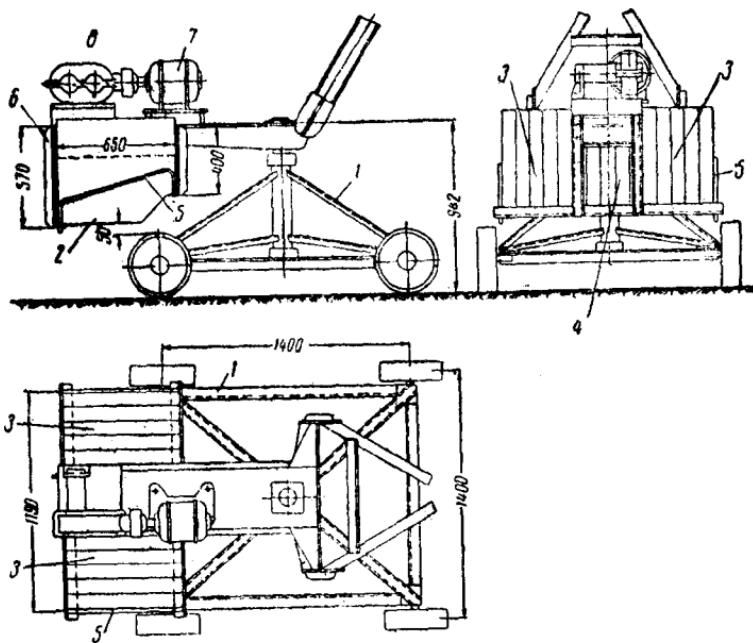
配置有钢筋混凝土块平衡锤的“先鋒牌”起重机行动小車
